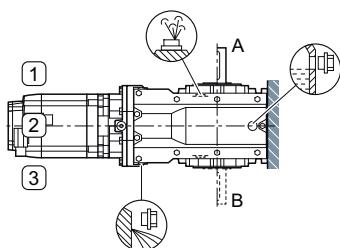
Einbaulagen für Servo-Kegelradgetriebemotor B, Fußausführung, Baugrößen 39 - 49, 2-stufig
